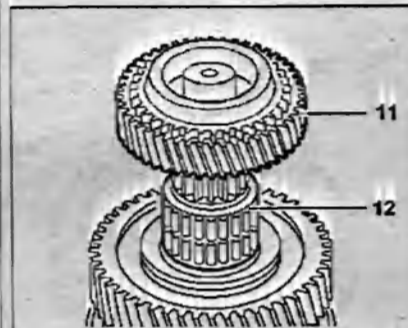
Снимите шестерню 11 3-й передачи и игольчатый подшипник 12.
